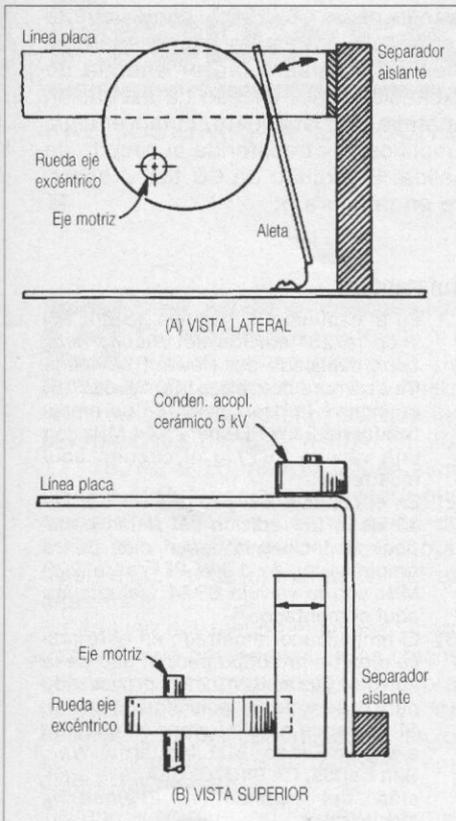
(A) Vista lateral de la aleta de sintonía de placa con rueda de eje excéntrico que se apoya contra la aleta dotada de gozne en su base. El conjunto se mueve desde el panel frontal a través de un dial vernier. (B) Vista superior del conjunto de placa mostrando la situación de los distintos componentes.
